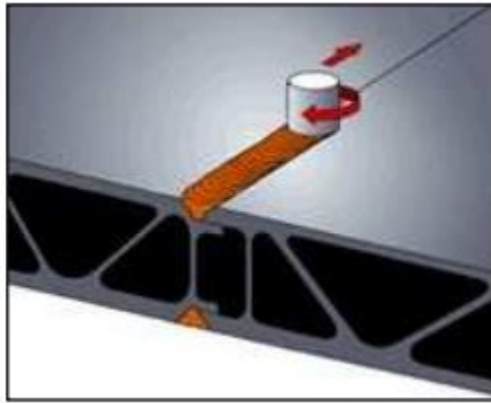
Technique de soudage des carrosseries des trains Hitachi
